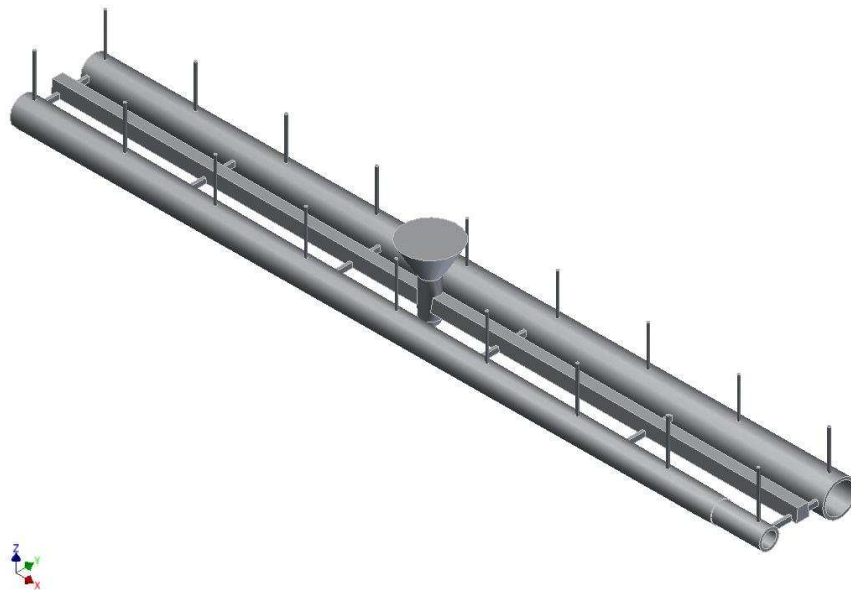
Modelo CAD de la pieza a ser obtenida en la caja 2 de fundición.
